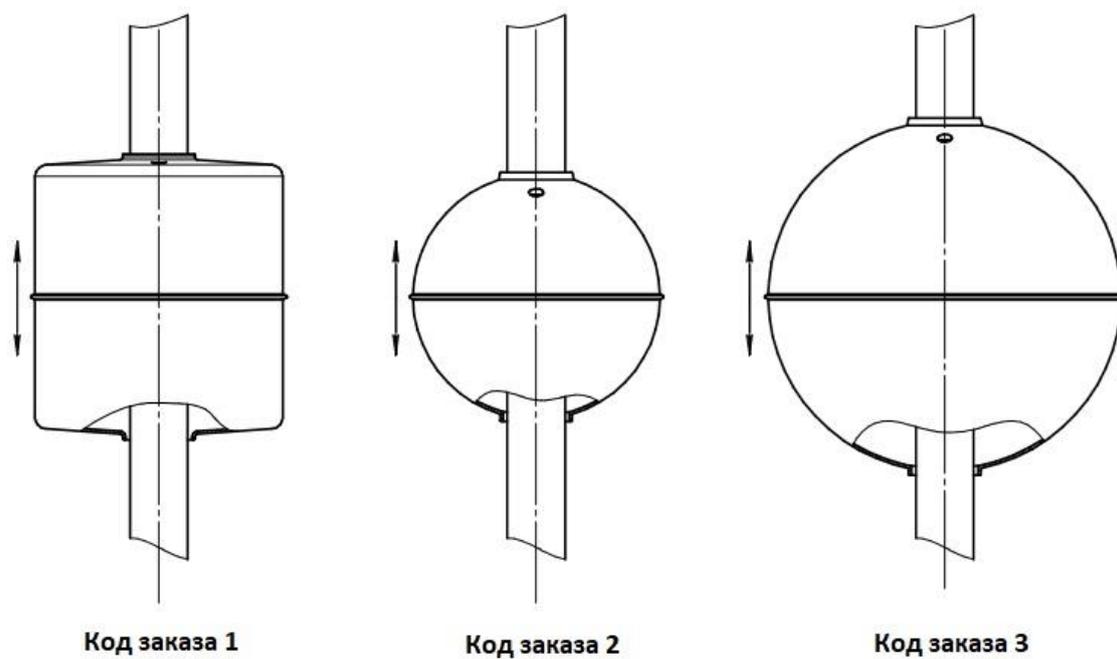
Монтажная часть ЭЛЕМЕР-УПП-11 с различными типами поплавков.
